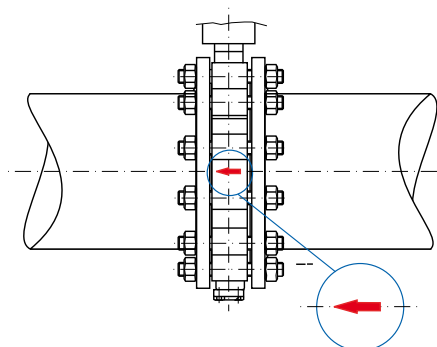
Oznaczenie kierunku preferowanego przepływu
